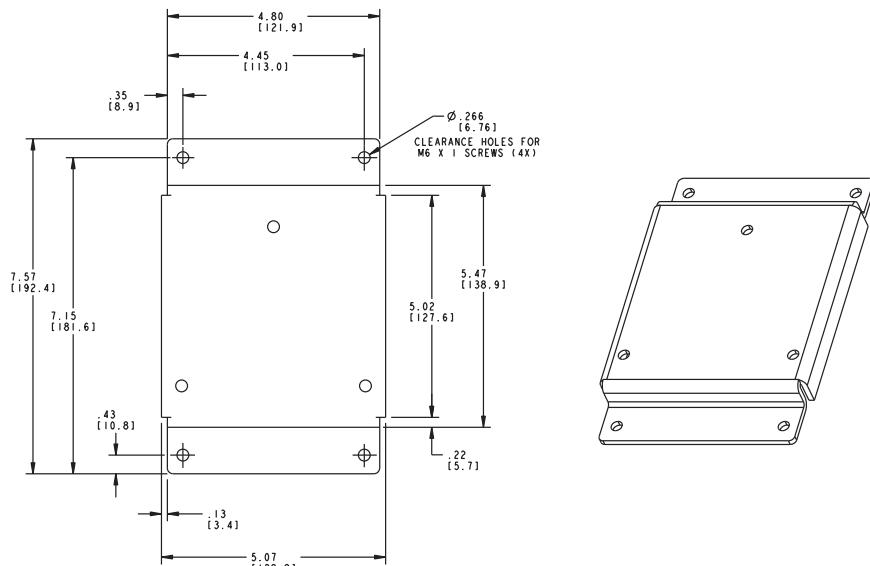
Soporte de montaje para caja de conexiones de aluminio
